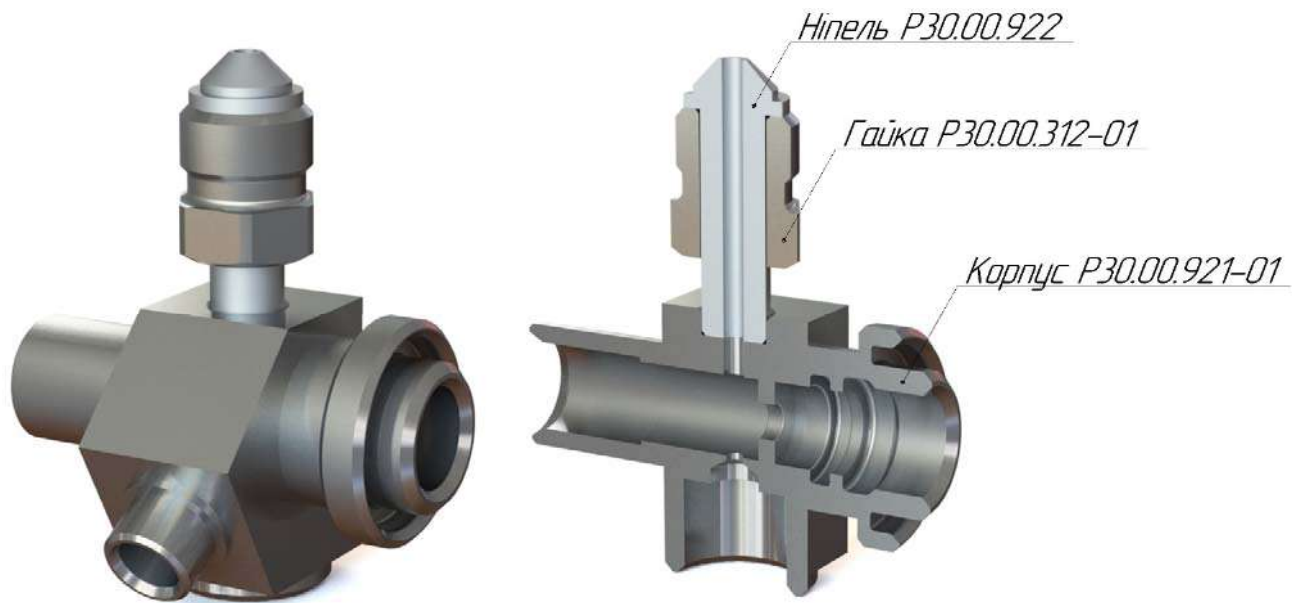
3D модель складальної одиниці типу корпус
